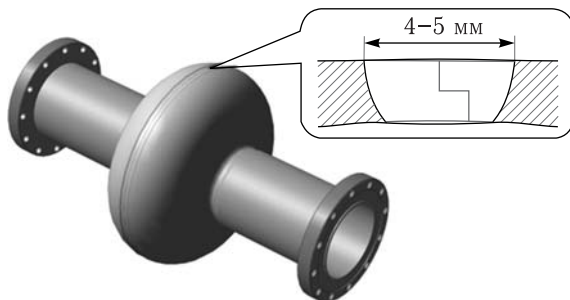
Внешний вид одноячеечного СВЧ-резонатора 1,3 ГГц и требуемая геометрия сварного шва экватора
